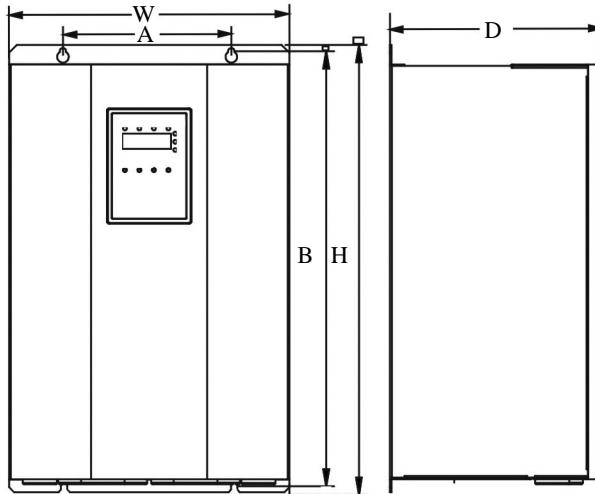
18.5kW~110kW 机型外形尺寸 (380V)
